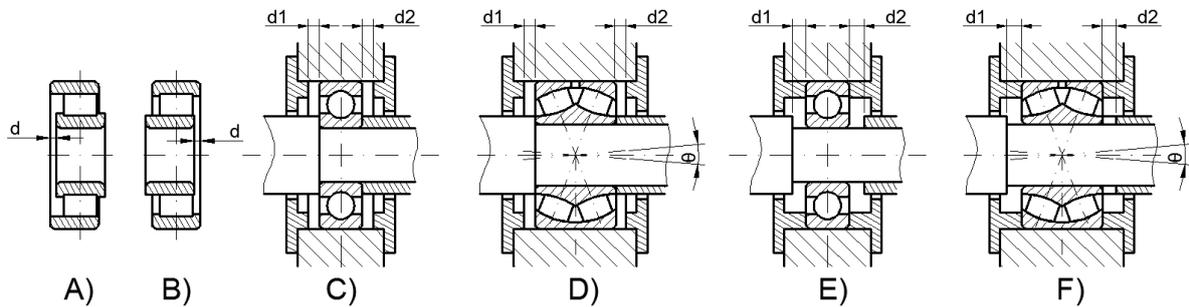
Soporte libre mediante desplazamiento d en el rodamiento del aro exterior A) o interior B); mediante ajuste deslizante en el alojamiento del soporte permite el desplazamiento d_1 , d_2 del rodamiento rígido de bolas C) o del rodamiento oscilante de rodillos E); mediante ajuste deslizante en el eje se dispone del desplazamiento d_1 , d_2 del rodamiento rígido de bolas E) o del rodamiento oscilante de rodillos F). El rodamiento oscilante D) o F) permite además cierto giro del eje.
